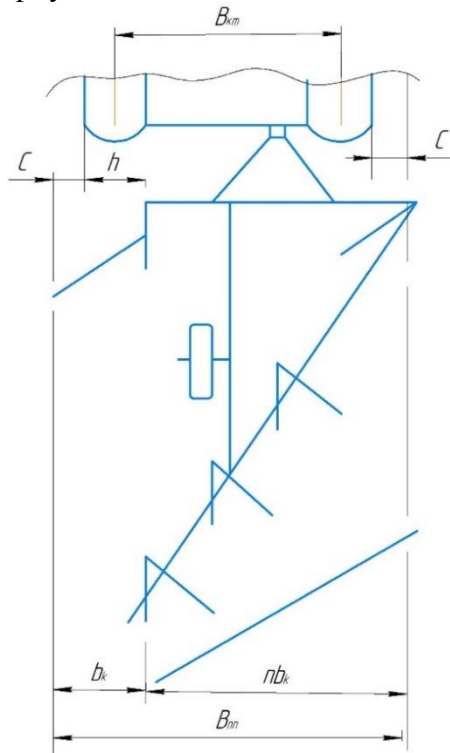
Схема до визначення ширини захвату плуга-плоскоріза
